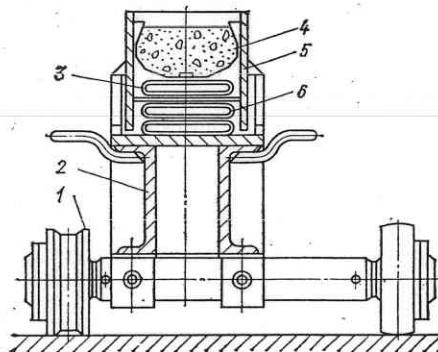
Флюсовая подушка ФП-1 для сварки продольных швов:
